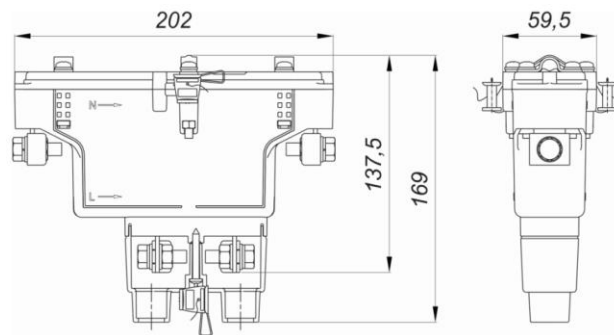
Общий вид и габаритные размеры счетчика в корпусе типа "Split".
